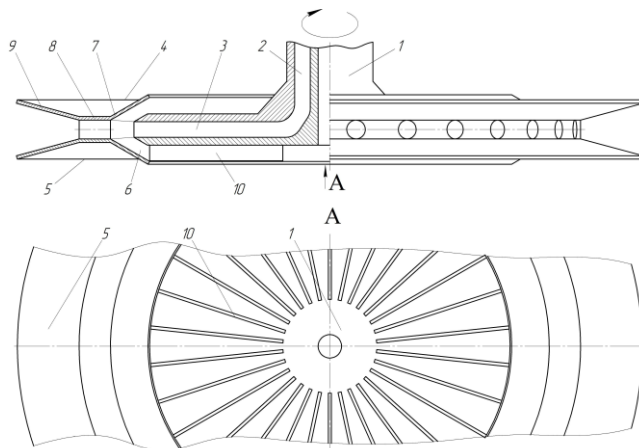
Розпилювальний диск з ежекційним пристроєм: 1 — корпус; 2 — розподільні канали; 3 — соплові отвори; 4 — верхня профільна пластина; 5 — нижня профільна пластина; 6 — зазор між корпусом диска та профільними пластинами; 7 — конфузورها частина; 8 — горловина; 9 — дифузор; 10 — радіальні лопаті
